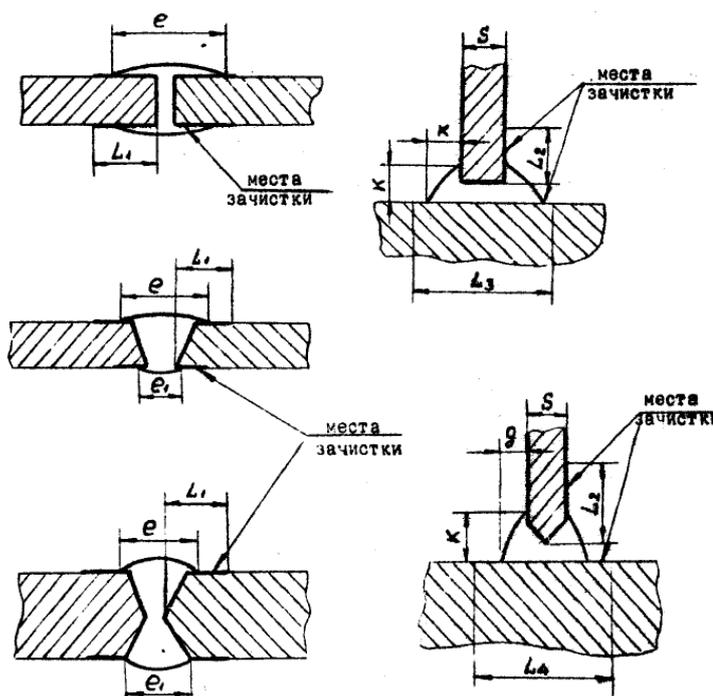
«Ширина зачищаемой поверхности кромок соединяемых деталей где: L – ширина зачищаемой поверхности; k – высота шва; e – ширина шва; s – толщина детали» [16].
